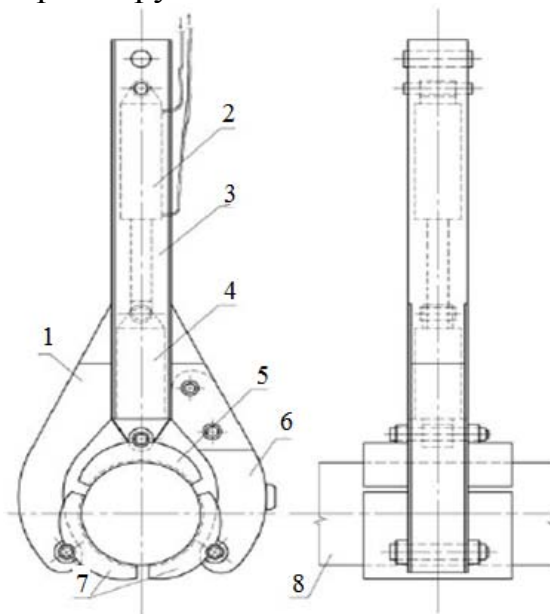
Схема гидравлического захватного устройства: 1 – корпус, 2 – гидроцилиндр, 3 – стойка корпуса, 4 – шток направляющий, 5, 7 – фрикционные накладки съёмные, 6 – затвор замыкающий, 8 – трубопровод
